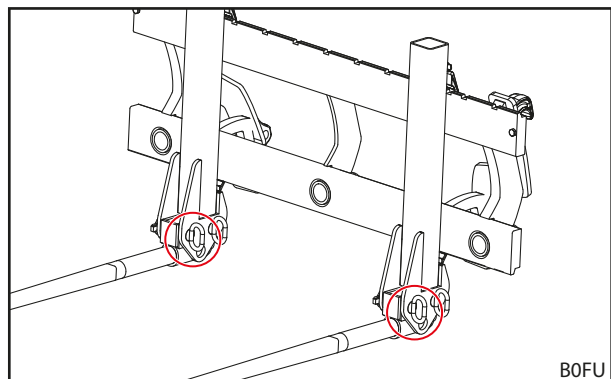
Точки смазки вилок для крупных тюков HS со складными зубьями
